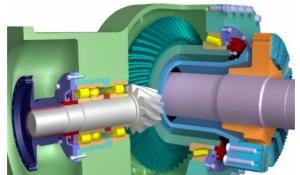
3D-модель редуктора колесной пары в разрезе
